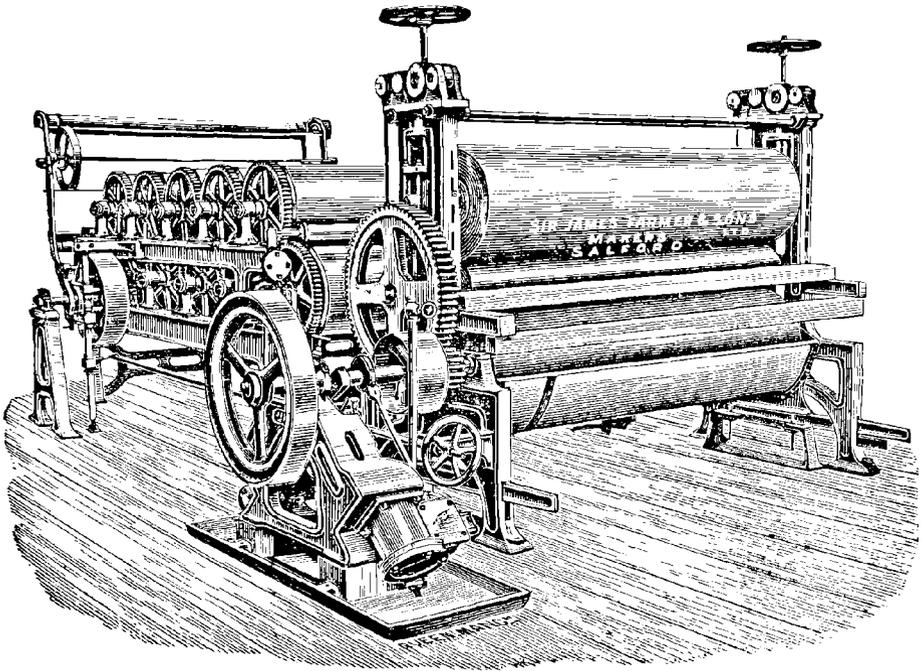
Machine à plaquer avec séchoir à vapeur à onze tambours, avec contact des deux côtés.
